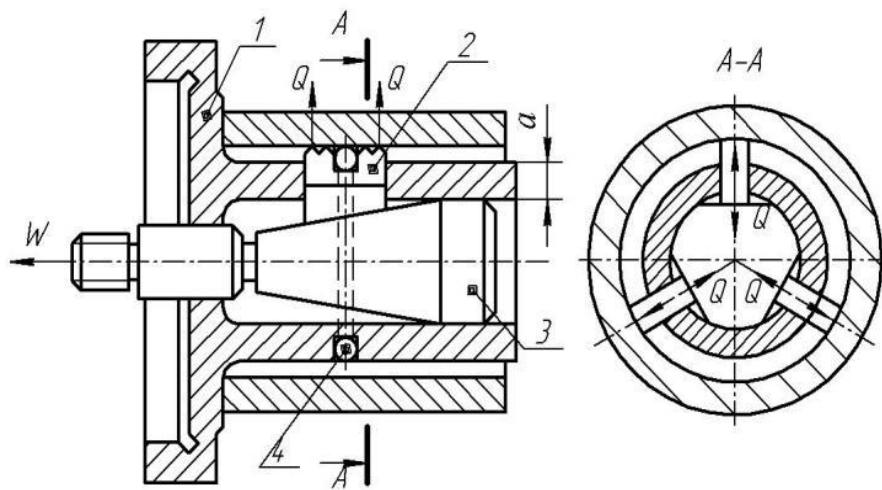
Схема клиноплунжерного токарного патрона:
